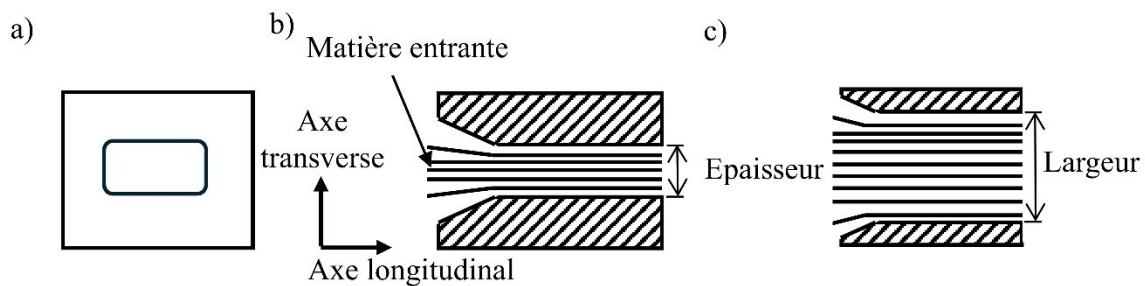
Schéma d'une filière de chauffe. a) Vue de Face, b) Vue de côté, c) Vue de dessus
